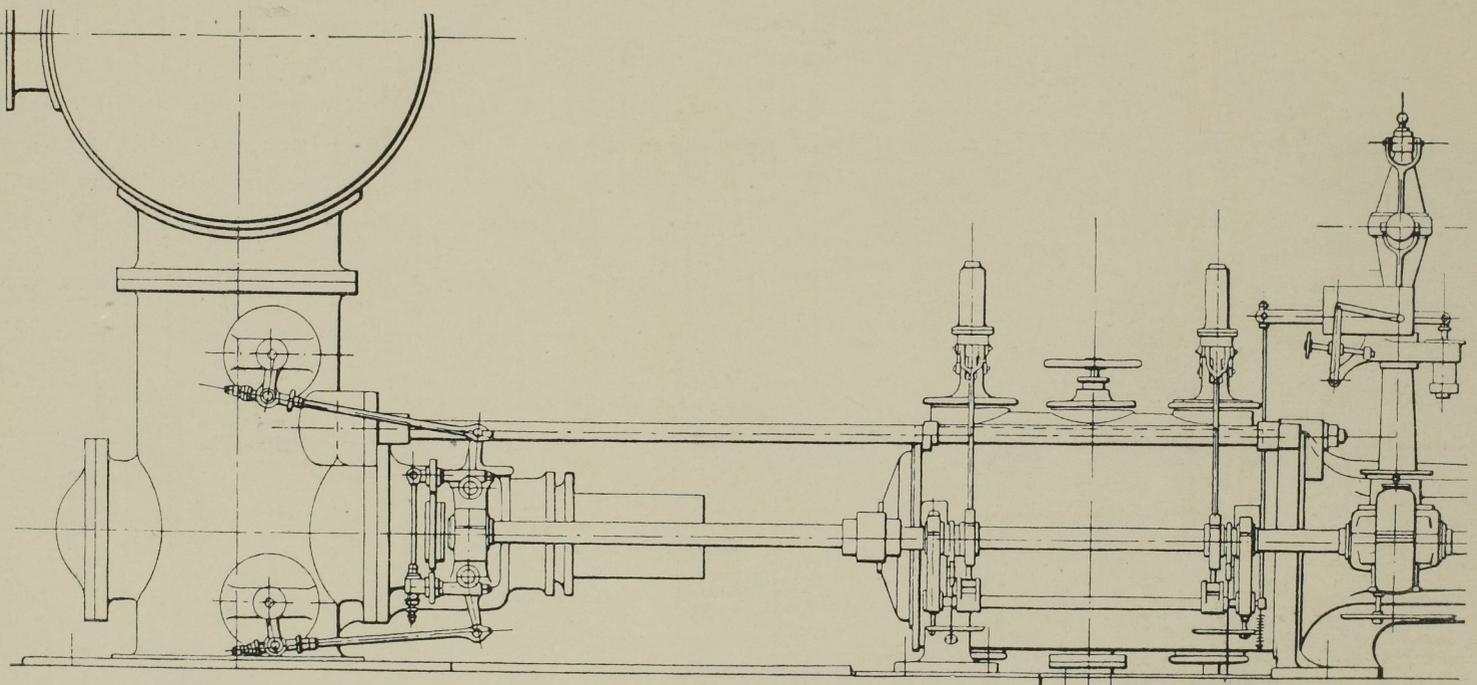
Seitenansicht der Dampf- und Pumpensteuerung. Massst. 1:60.
